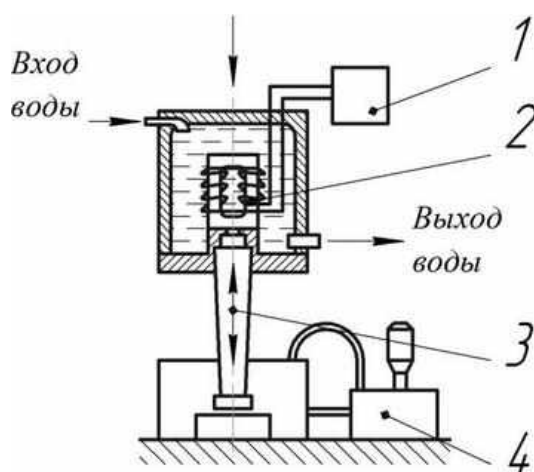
Схема установки для ультразвуковой размерной обработки
